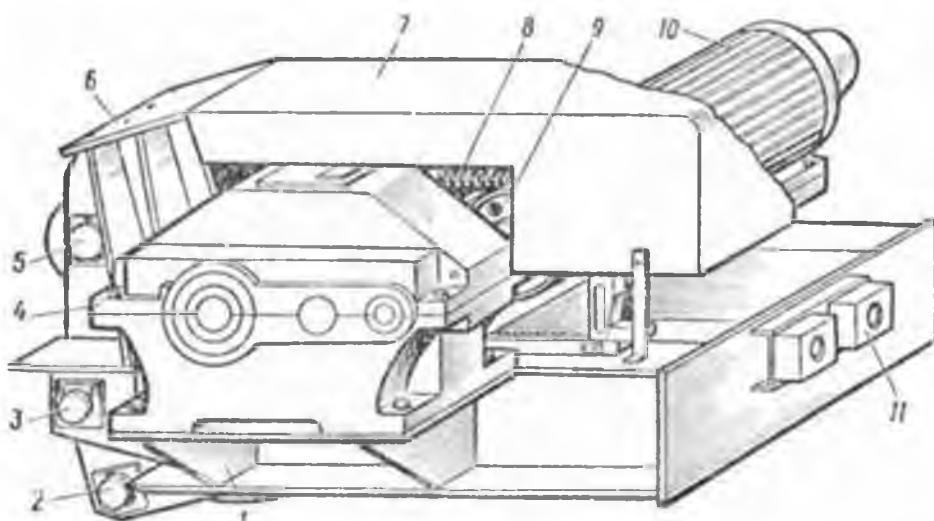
Опорний візок крана ККТ-5: 1 - рама; 2 - вісь рейкового захоплення; 3 - вал кріплення опорної стяжки; 4 - редуктор; 5 - вісь монтажних блоків; 6 - плита з'єднання зі стійкою; 7 - кожух; 8 - гальмівний пристрій; 9 - шків; 10 - електродвигун; 11 - гумовий буфер
